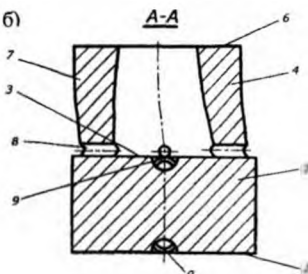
Схема кольцевой трамбовки, обеспечивающей двухстадийное уплотнение.
